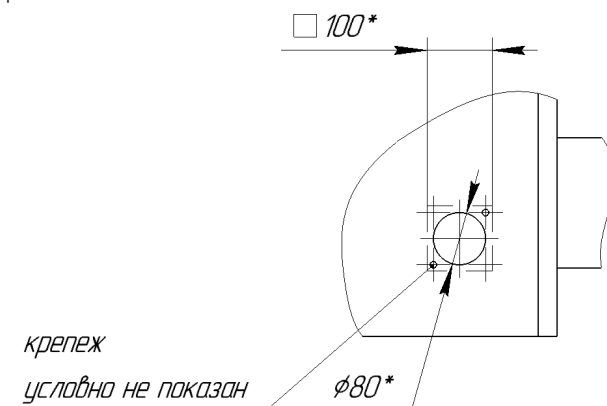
Вид снизу выключателя. Размеры пластины
